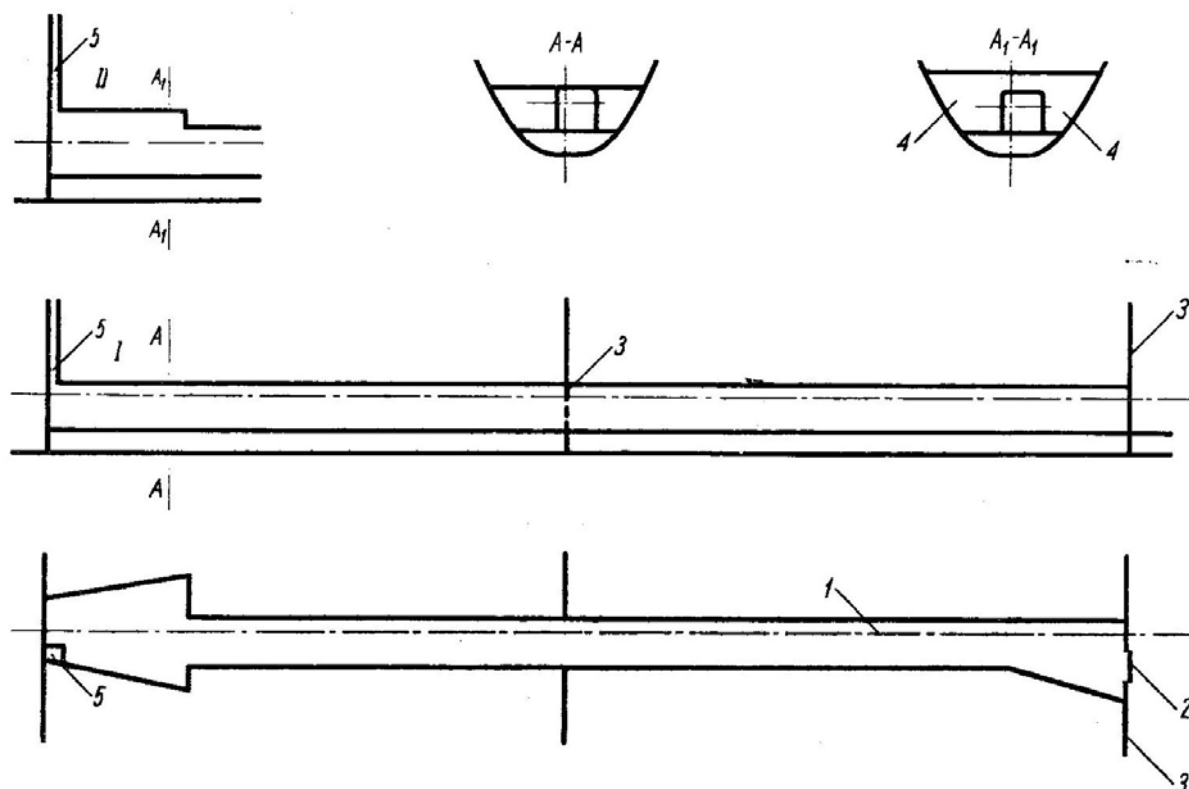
Typowe konfiguracje przekroju poprzecznego tunelu linii wałów
